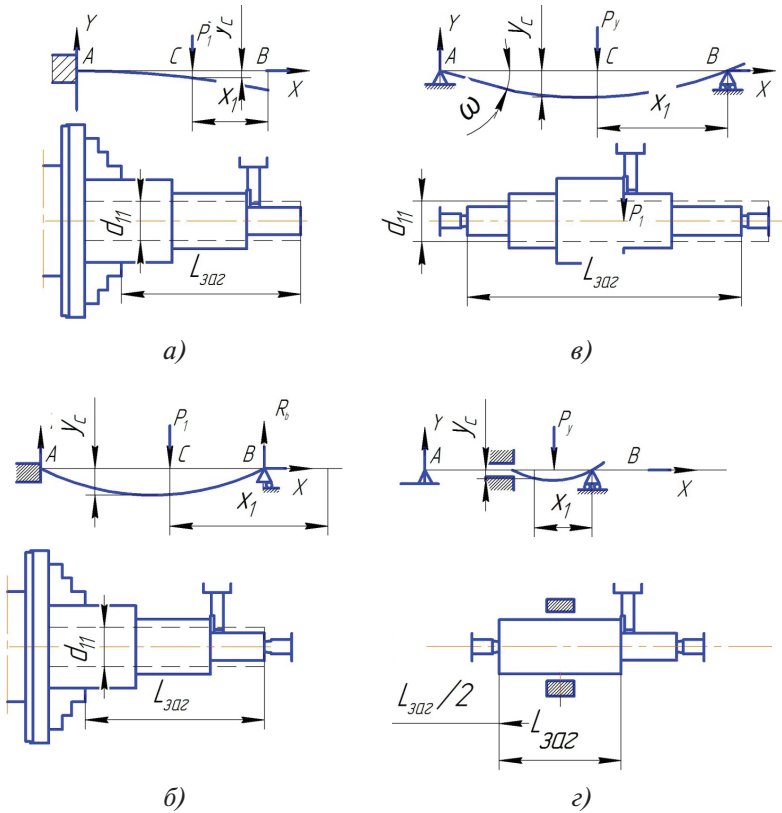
Схемы способов установки деталей на токарных станках:
